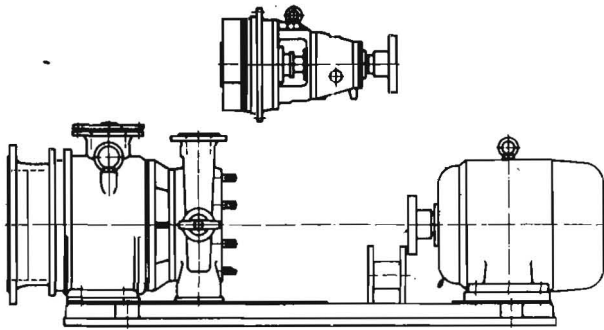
Schematische Darstellung des Ausbaues des Lagerträgers bei einer Baugröße der Baureihe KRCH — Ausführung „Gülle“ —
